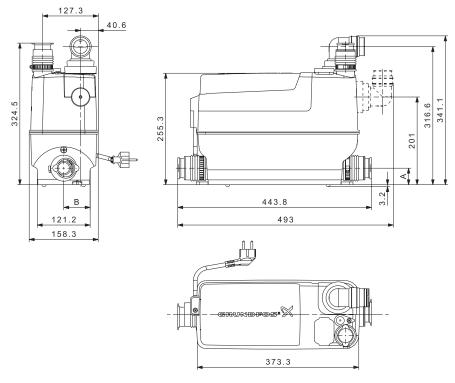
Габаритные размеры, SOLOLIFT2 C-3
